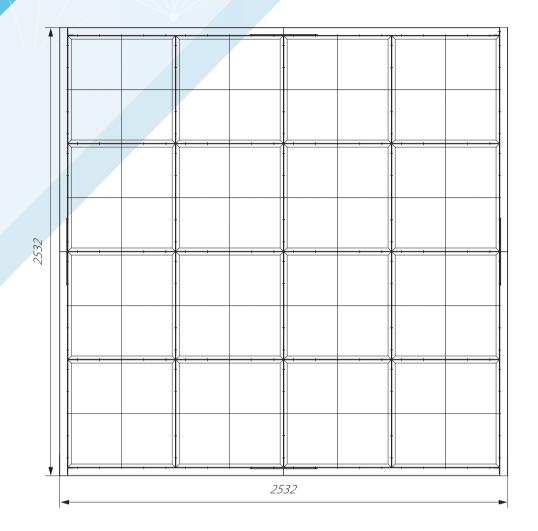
Общий вид фильтра карманного для очистки приточного воздуха ФОВПЭ-18560 PE 271.00.00.000.
